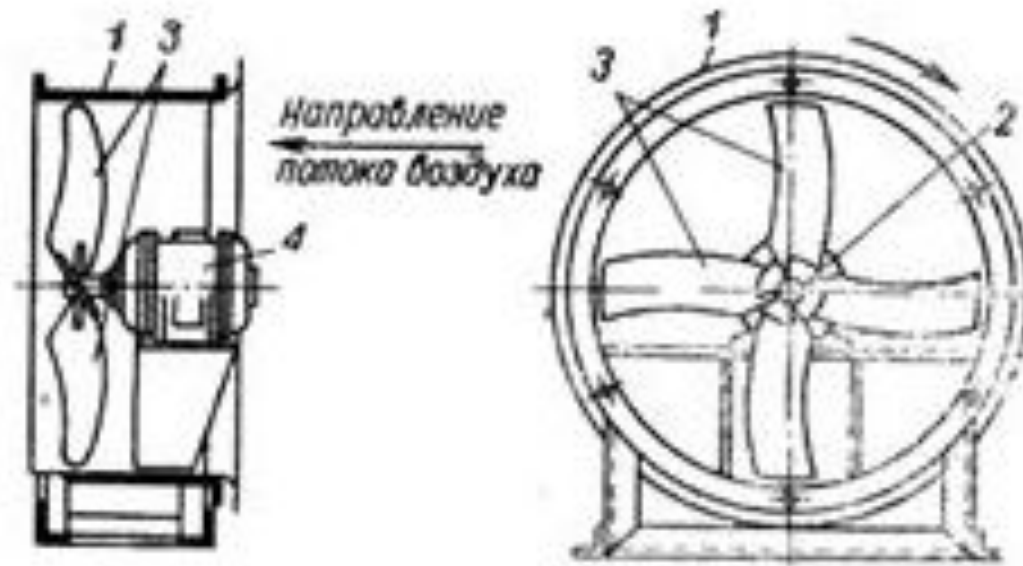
Осевой вентилятор ЦАГИ 1 – кожух (обечайка) из листовой стали; 2 – втулка; 3 – лопастное колесо; 4 – электродвигатель
